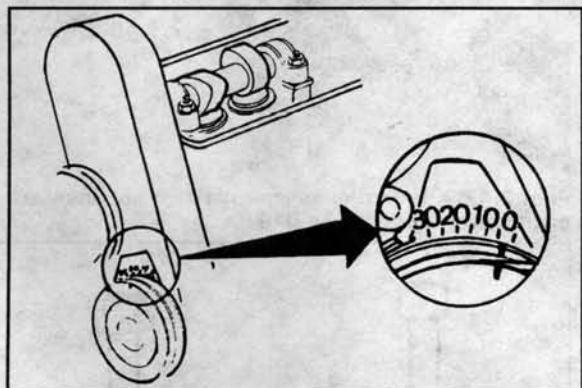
Установка поршня 1-го цилиндра двигателя В19 в положении ВМТ
